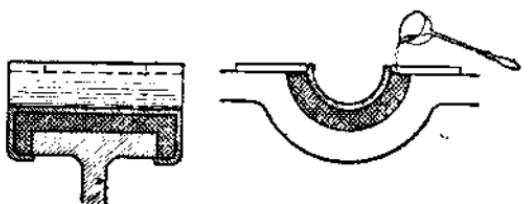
Приспособление для заливки коренных подшипников трактора «Фордзон».
